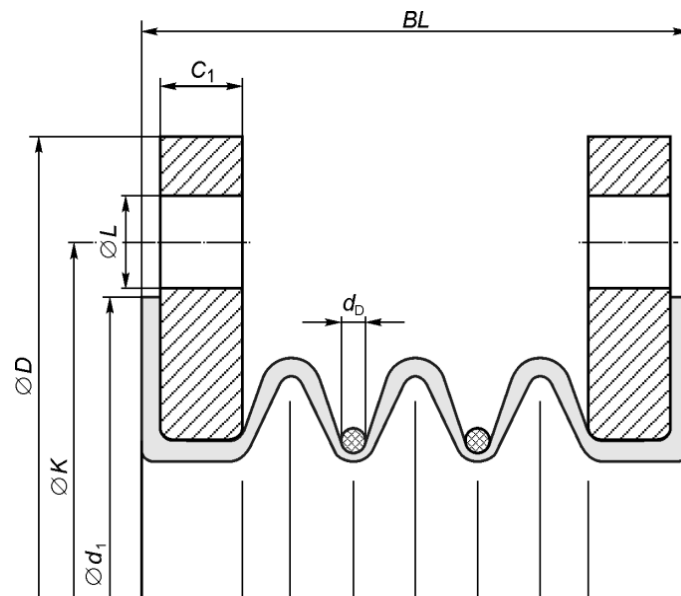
Skizze eines PTFE-Axialkompensators; Beispiel für 3-wellige Ausführung
